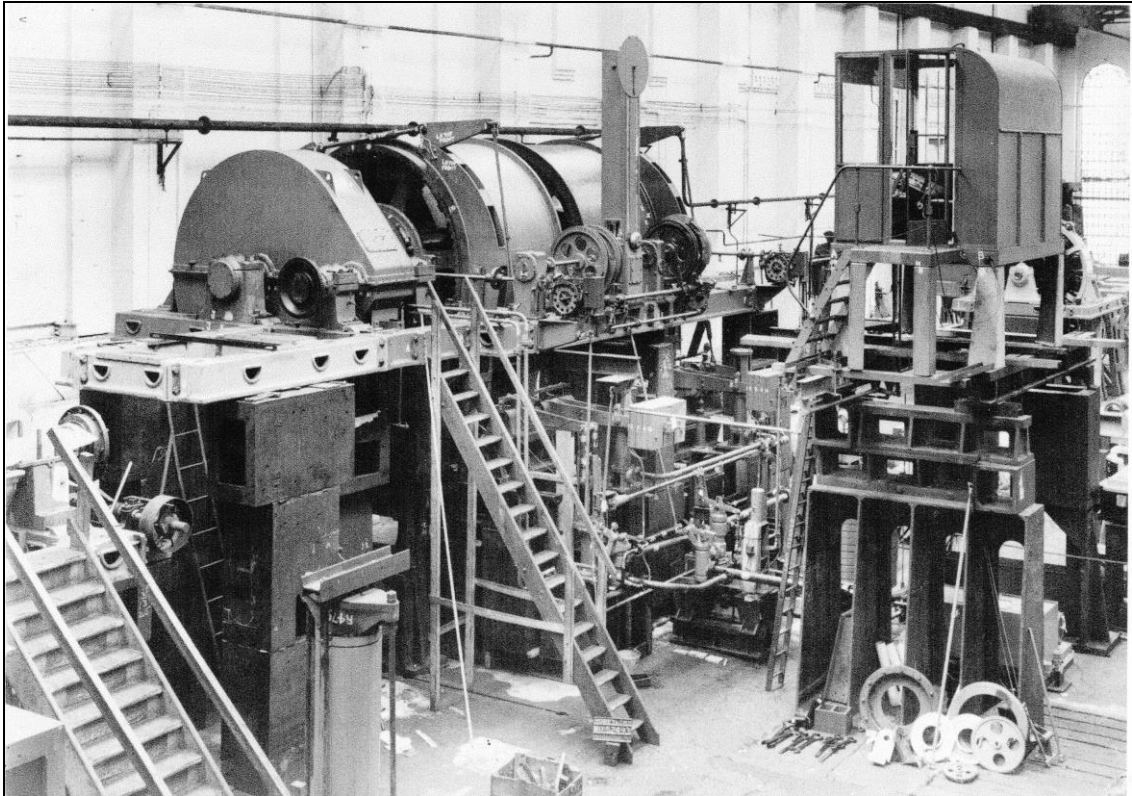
Máquina de extracción Robey, en construcción en Inglaterra, 1954 (Fot. Archivo Celan).
